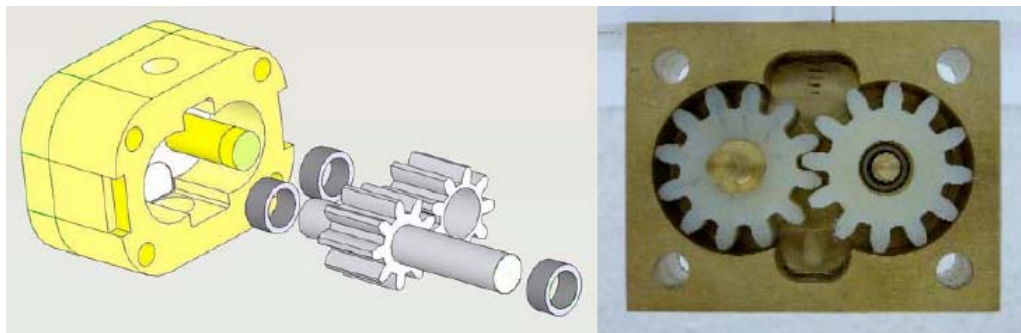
Subensamble del prototipo de micromotor hidráulico de dos engranes
